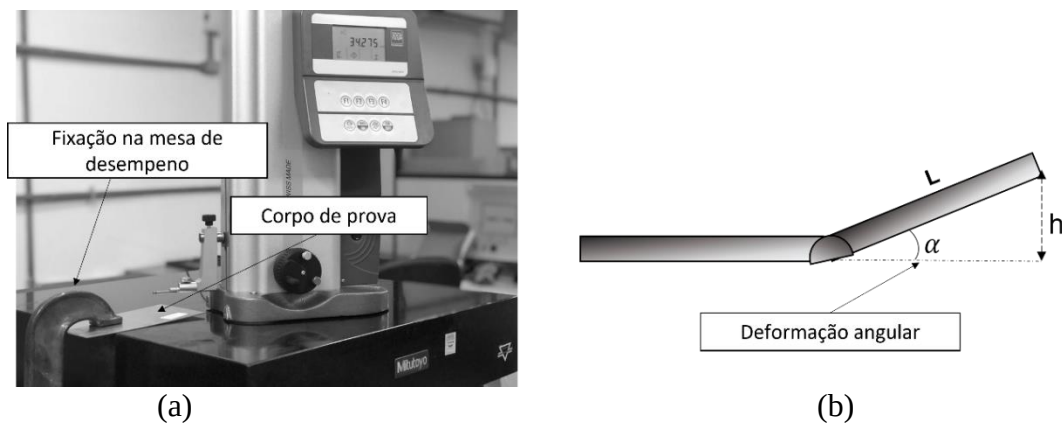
Medição de deformação angular dos corpos de prova soldados a laser:
